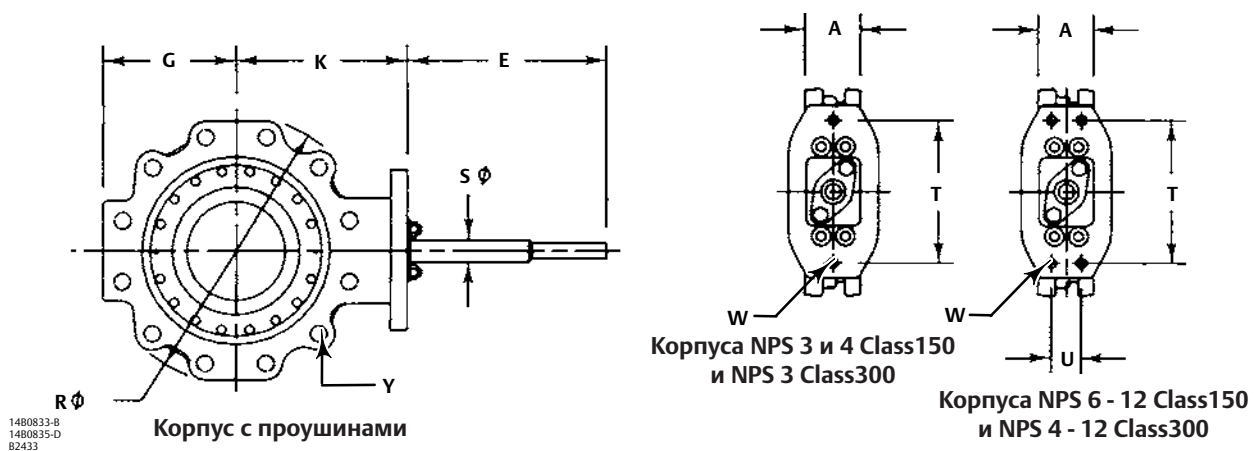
Размеры затвора 8560 со шлицевым валом
